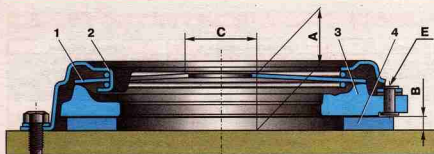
Контроль ведущей части сцепления: 1 — нажимная пружина; 2 — кожух сцепления; 3 — нажимный диск; 4 — промежуточное кольцо; А — контрольный размер; В — толщина промежуточного кольца; С — диаметр; Е — контрольная точка
